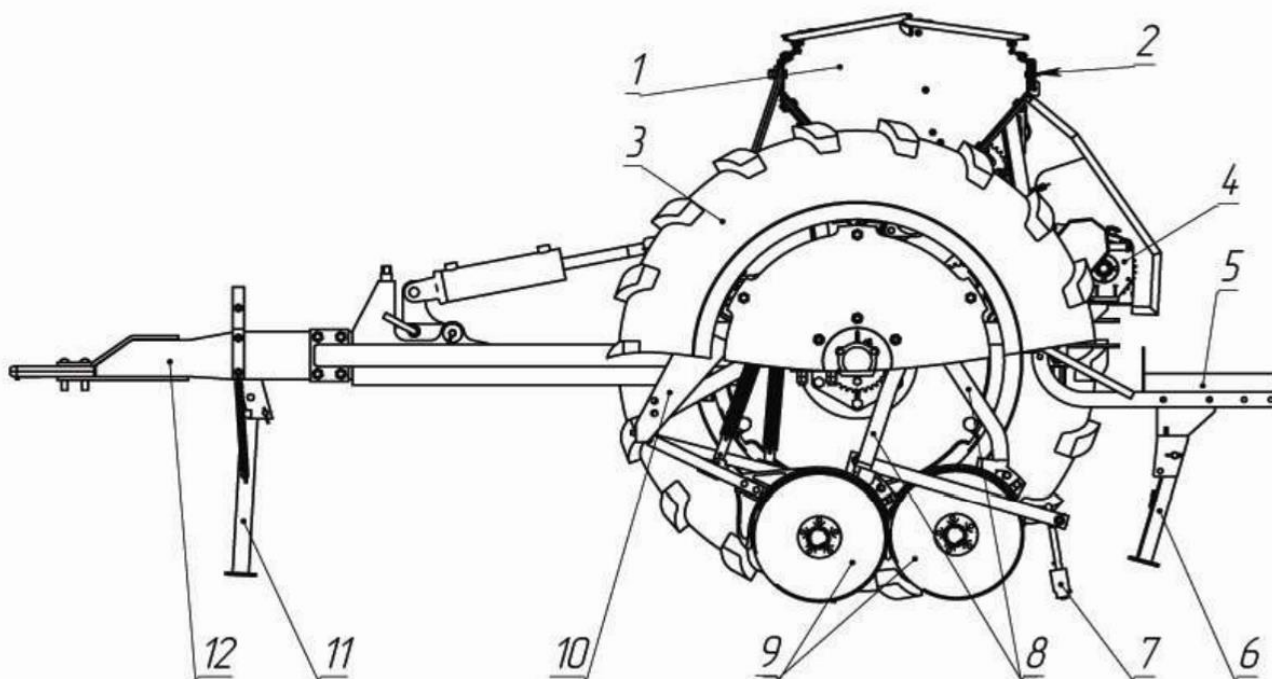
Схема сеялки СЗ-3,6А: 1 – зернотуковый ящик; 2 – световозвращатель; 3 – колесо; 4 – механизм передач; 5 – подножка; 6 – подставка; 7 – загортач; 8 – семяпровод; 9 – сошник; 10 – рама; 11 – подножка; 12 – сница
